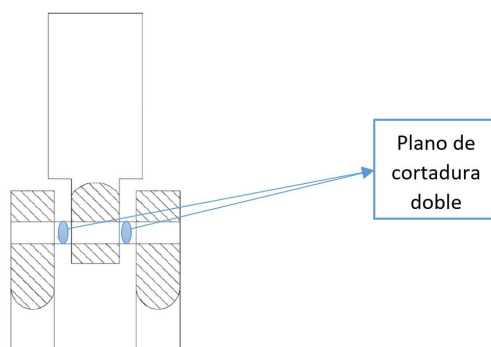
Croquis de un esfuerzo a cortante en un plano doble
